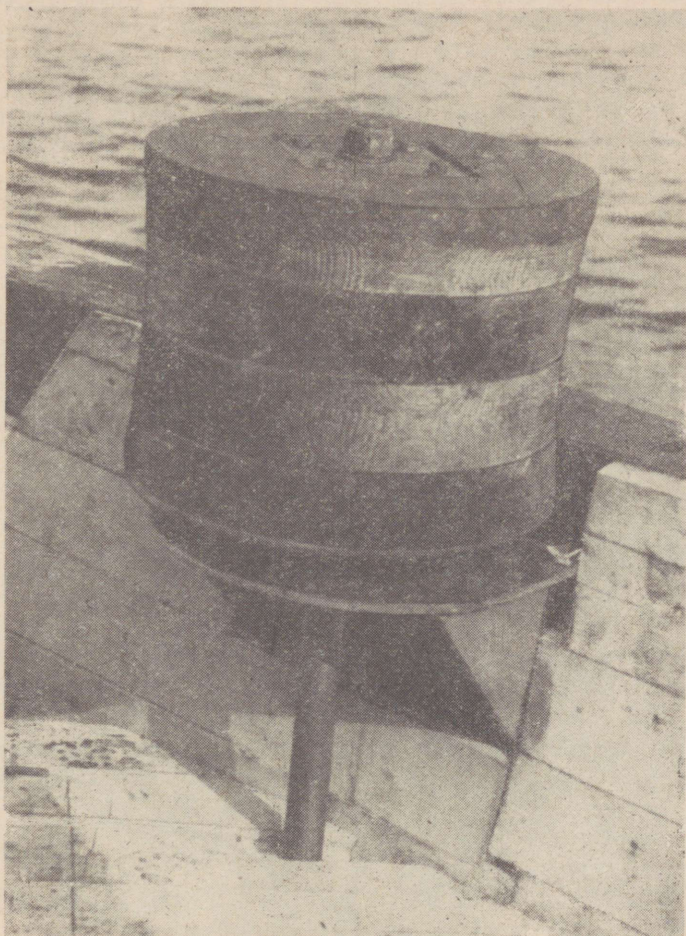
Механизм для выборки буйковых поводцов, предложенный тов. Селяниновым.
